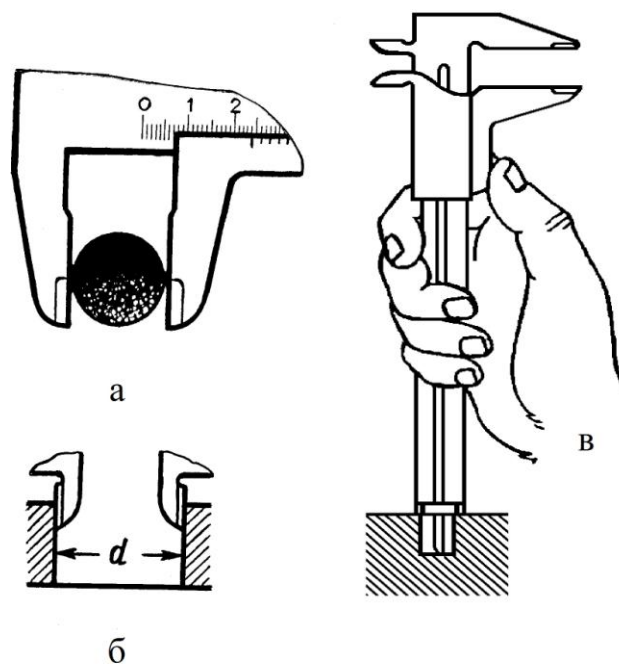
Измерение штангенциркулем наружных размеров (а),
